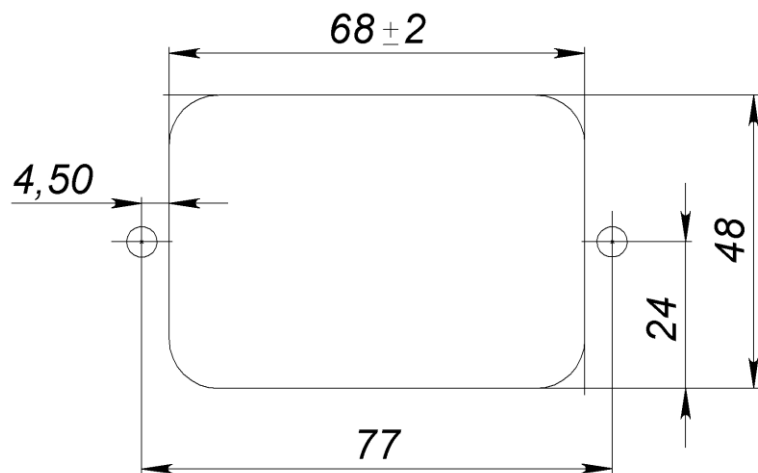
Разметка под установку видеокмеры EVM1-IP2-WM
